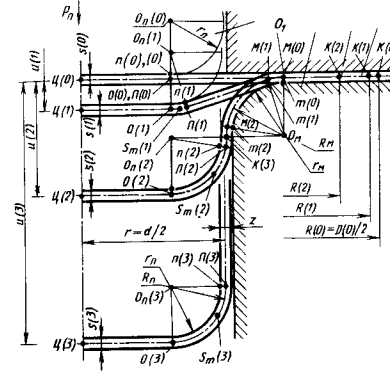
Кинематика формоизменения заготовки при вытяжке
